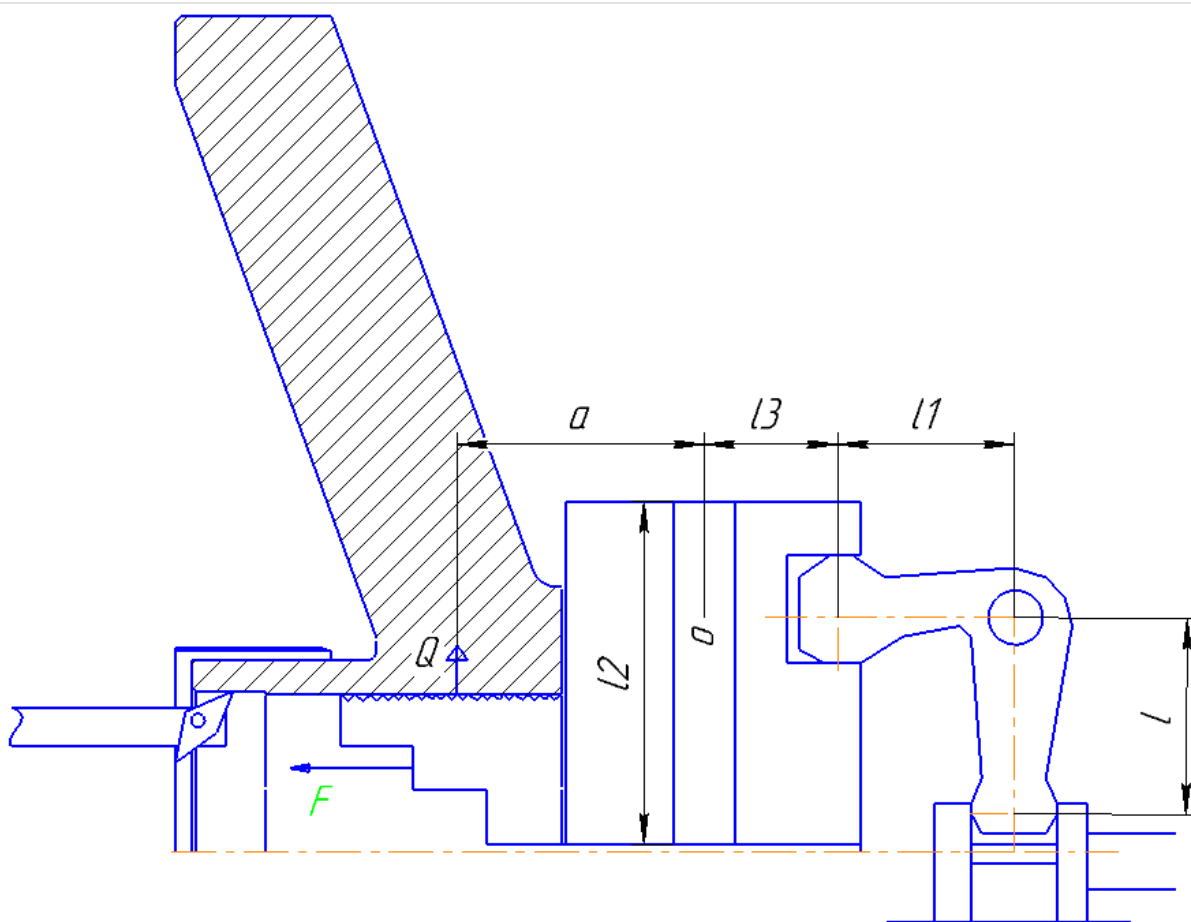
Схема кулачкового патрона для расчета силы на штоке пневматического привода
